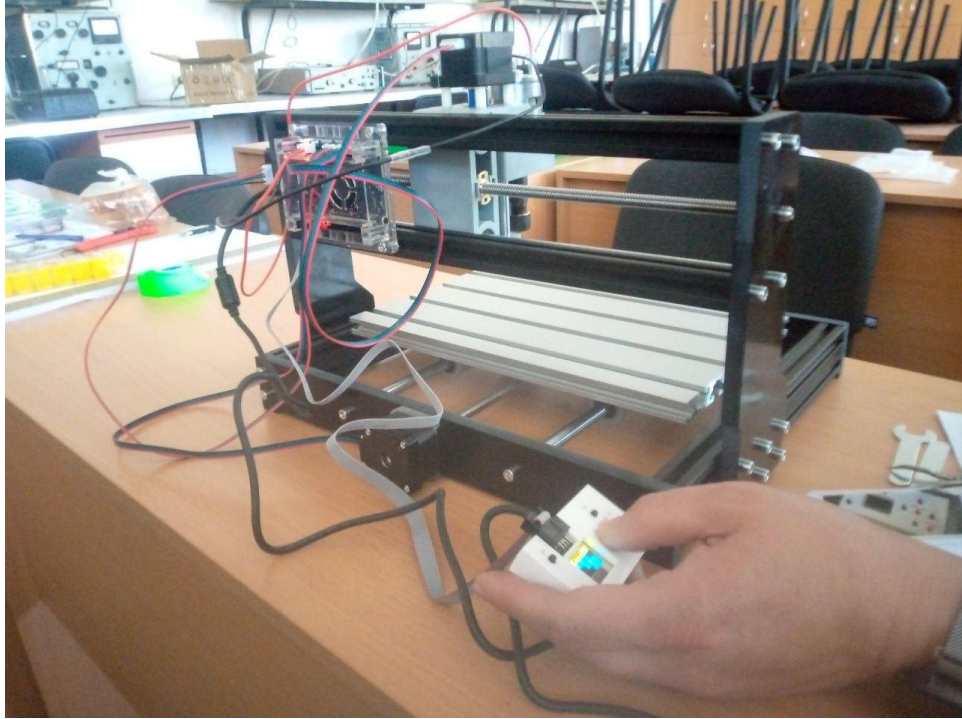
Фрезерний станок для виготовлення тестової плати
